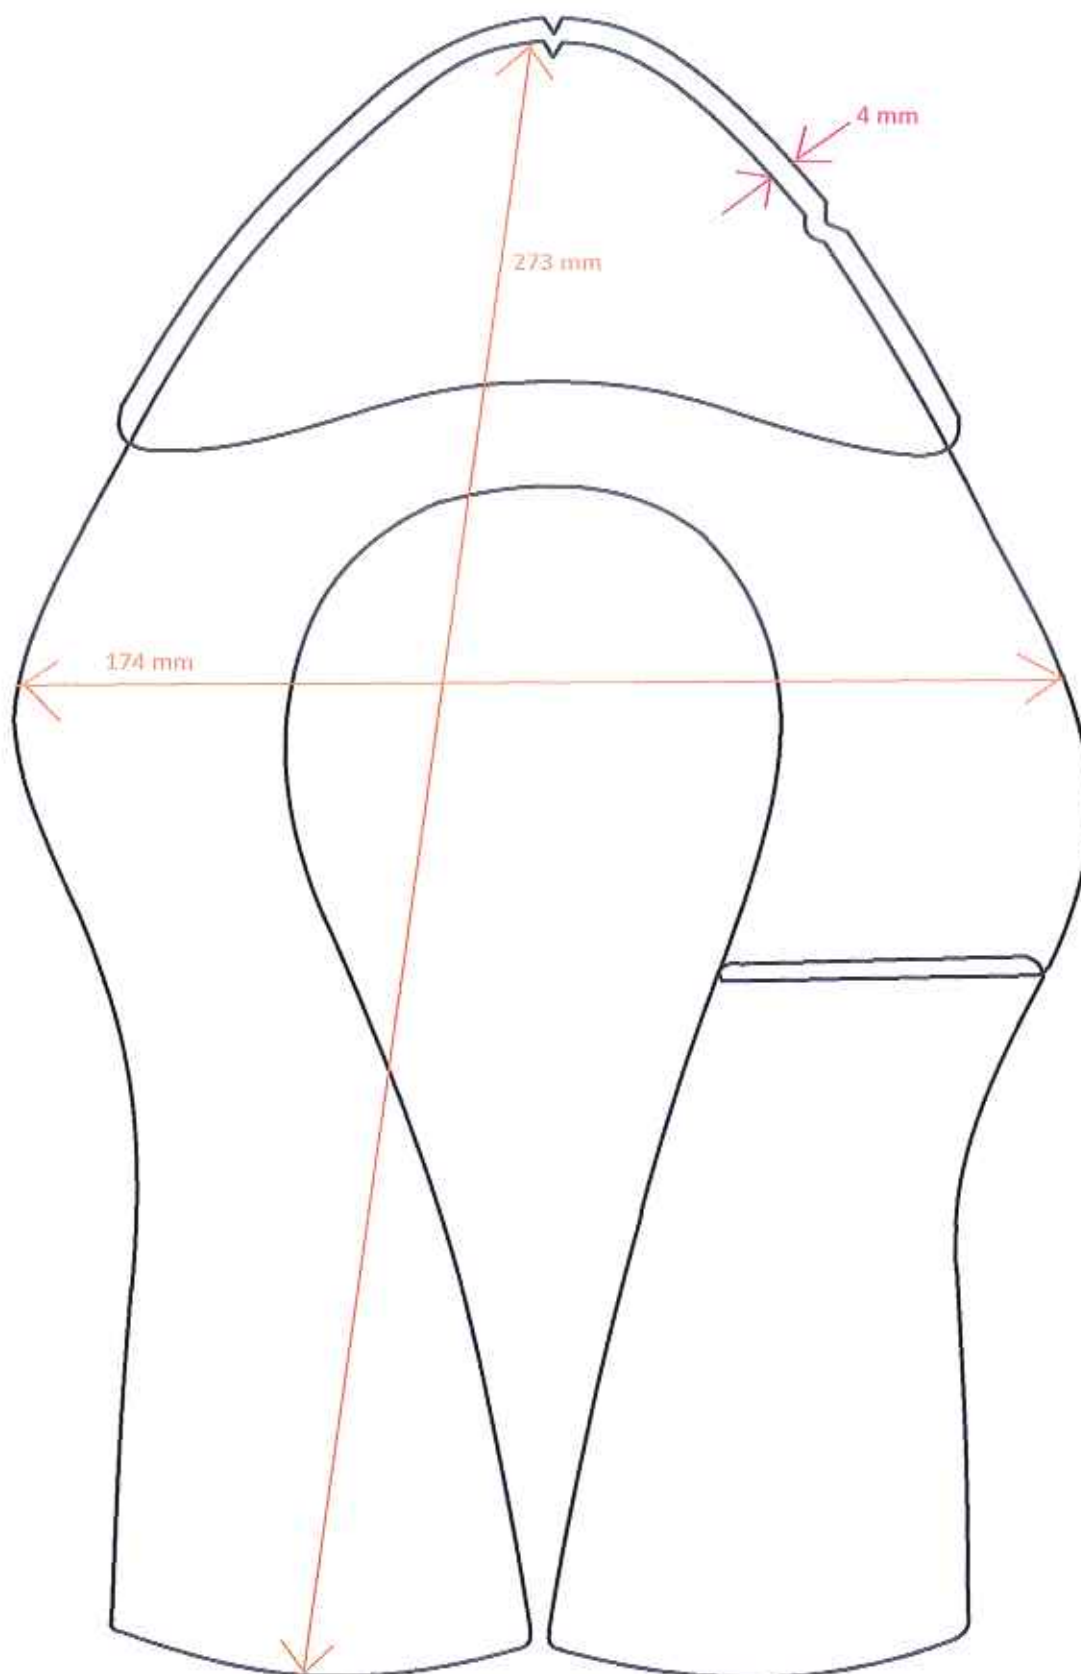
Rysunek złożeniowy elementów wierzchnich w rozm. 37
